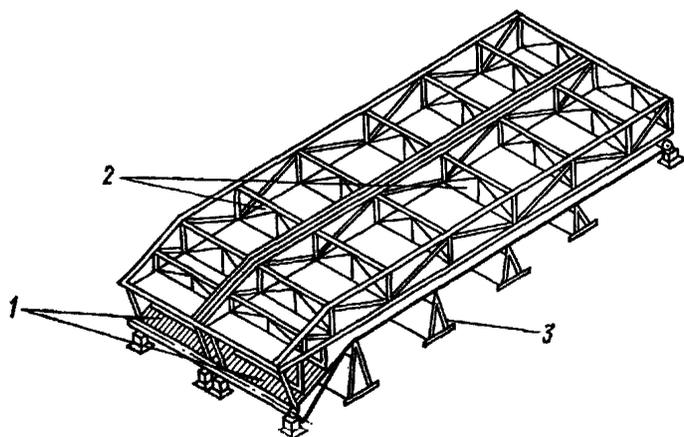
Укрупнение топочных блоков (поставка поверхности нагрева с каркасом)
